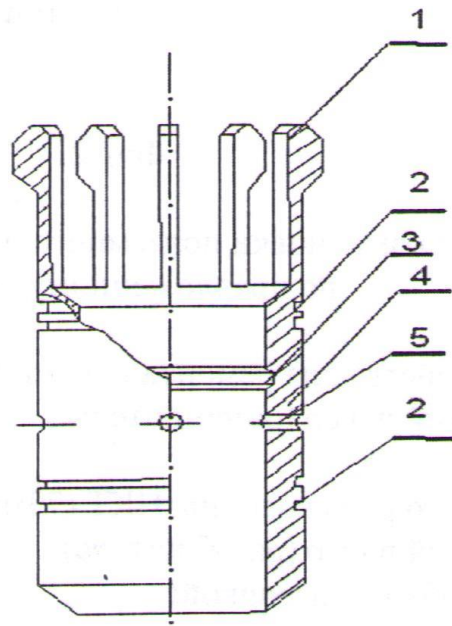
Извлекаемый забойный штуцер (дополнительно введенный): 1 - упругий замковый фиксатор; 2 - канавки для уплотнительных колец; 3 - захватное место для работы с канатной техникой; 4 - корпус штуцера; 5 - калиброванные отверстия штуцера
